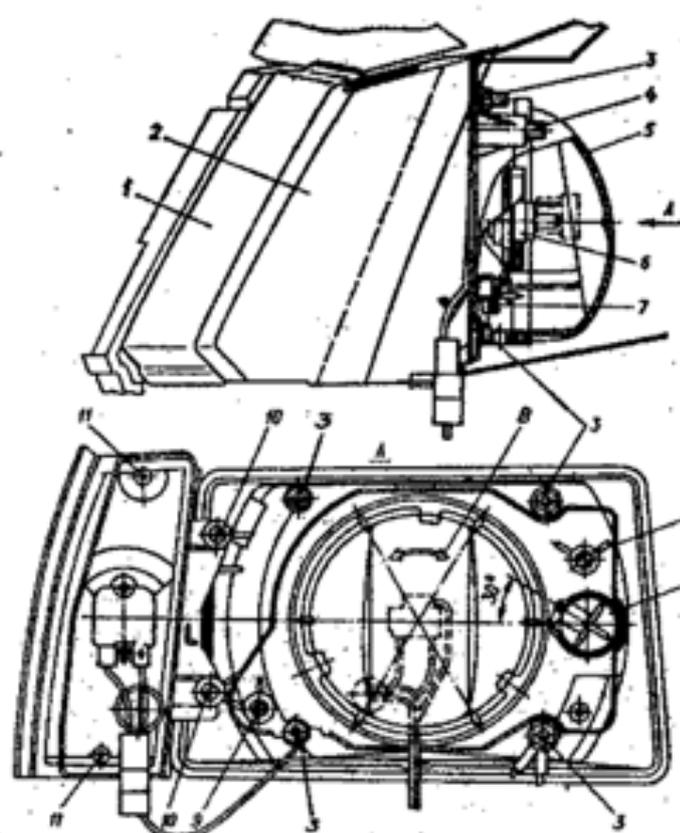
Блок-фара: 1 - блок-фара; 2 - указатель поворота; 3 - гайка крепления фары; 4 - винт вертикальной регулировки; 5 - крышка; 6 - лампа фары; 7 - лампа стояночного света; 8 - заглушка корректировки светового пучка в зависимости от нагрузки автомобиля; 9 - винт горизонтальной регулировки; 10 - винт крепления указателя поворота; 11 - винт крепления рассеивателя указателя поворота
